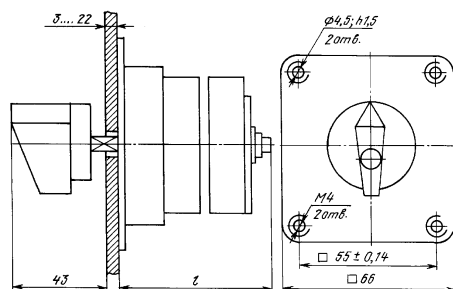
Габаритные, установочные размеры и масса переключателей типа ПКУЗ 11:
